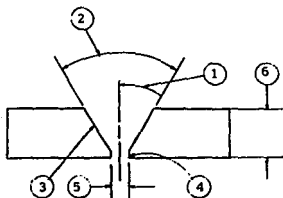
Detalles de la soldadura de ranura.
